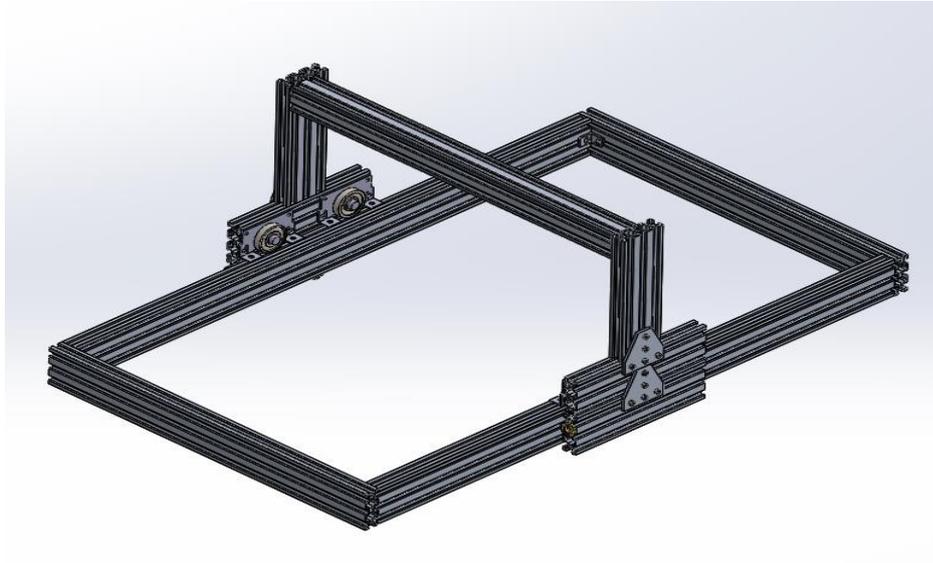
Partie principale du bâti de la machine en aluminium de la machine CNC 5 axes
